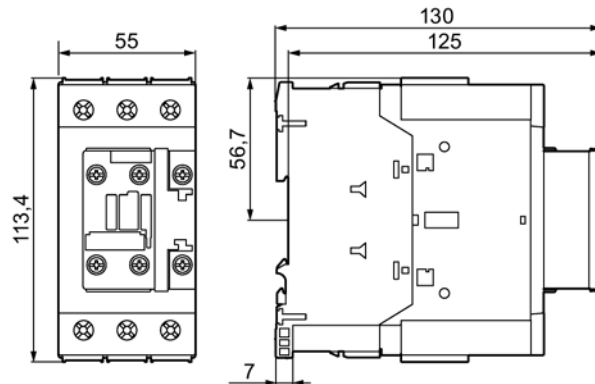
Schütz 3RT2.3.-1 (Schraubanschlusstechnik)
